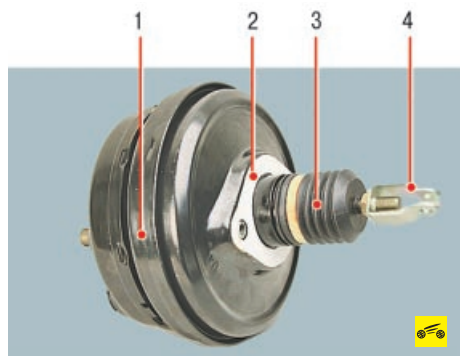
Вакуумный усилитель: 1 – корпус усилителя; 2 – уплотнительная прокладка корпуса; 3 – защитный чехол корпуса управляющего клапана; 4 – вилка толкателя
